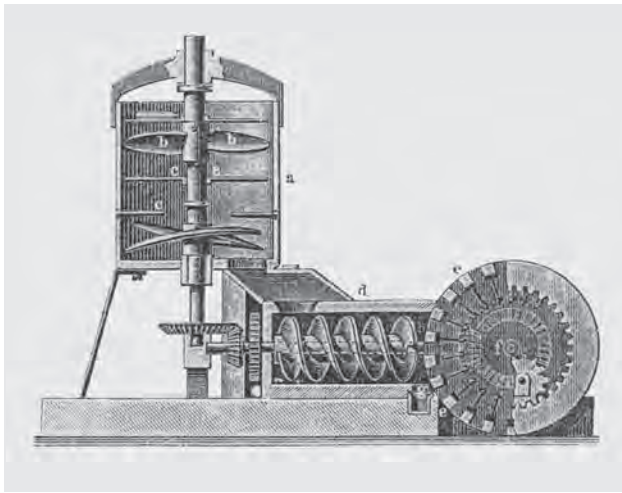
Ziegelmaschine mit Tonschneider und Schnecke zum Einpressen des Tons in ein Formenrad
